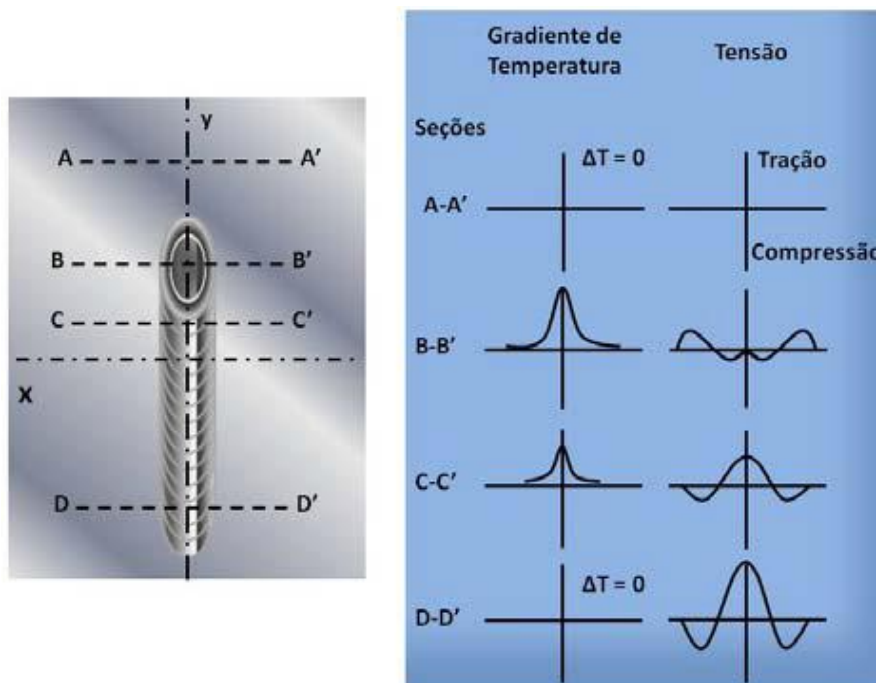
Desenvolvimento de tensões residuais longitudinais durante a soldagem.
